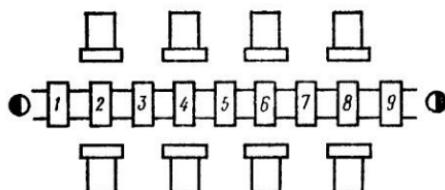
Схема автоматической линии из четырех станков с одинаковым положением обрабатываемой заготовки:
